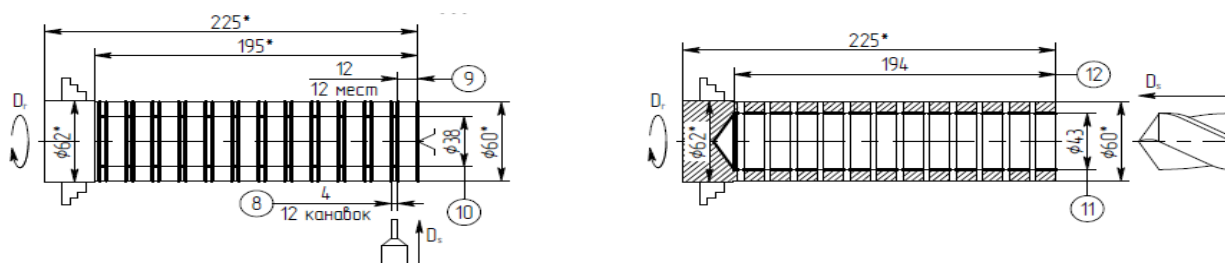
Токарная обработка - получение кольцевых заготовок из круглого проката
